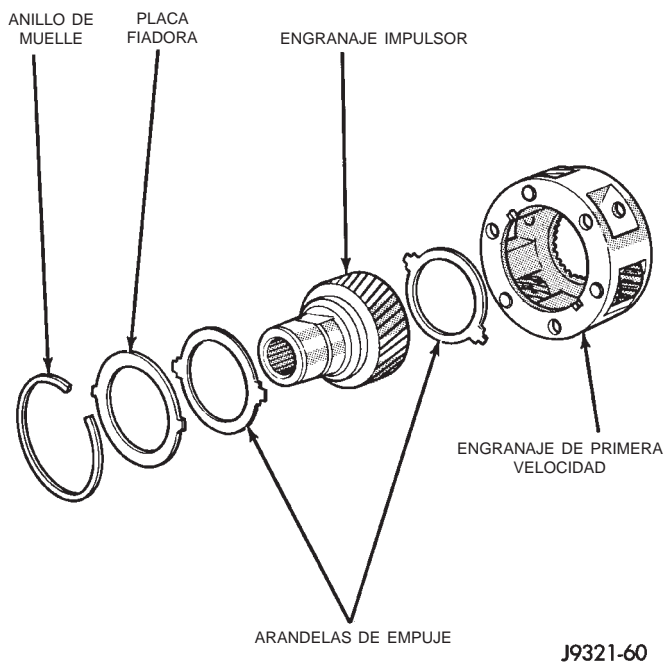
Componentes del engranaje impulsor y de primera velocidad
